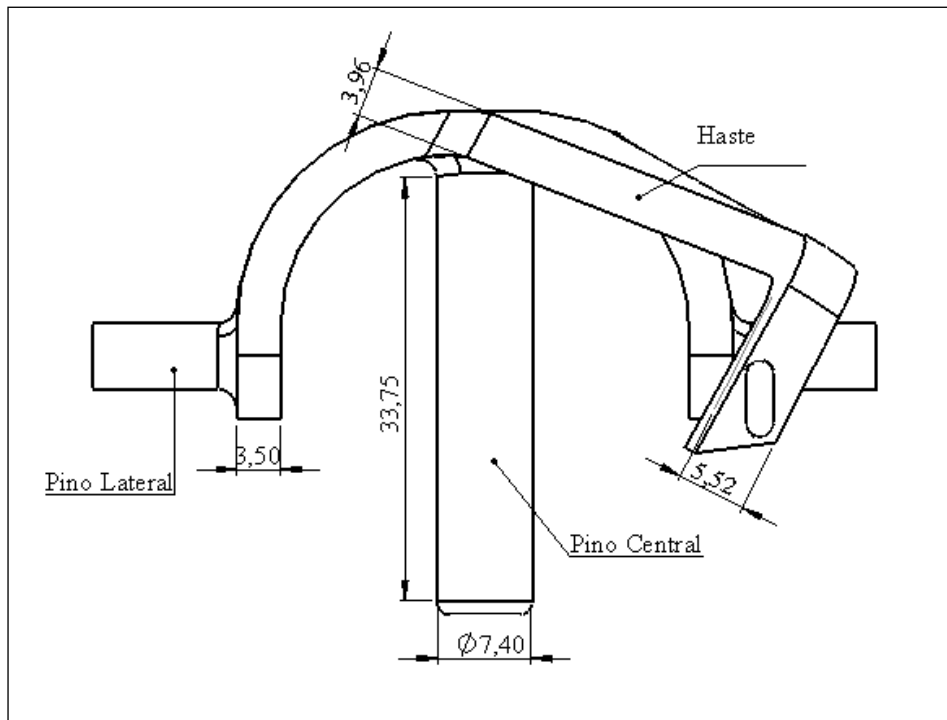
Dimensões, em milímetros, da estrutura de encaixe do comando em vista posterior
